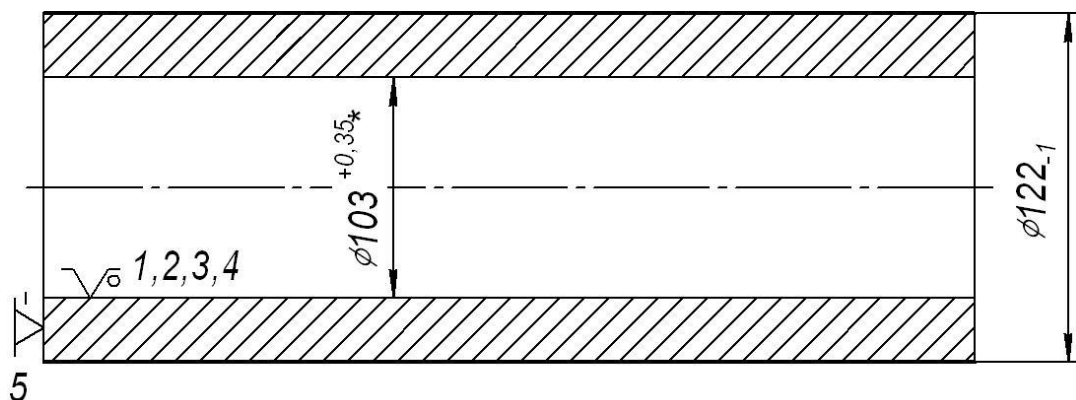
Схема базування заготовки на операції 011 «Токарно-гвинторізна»
